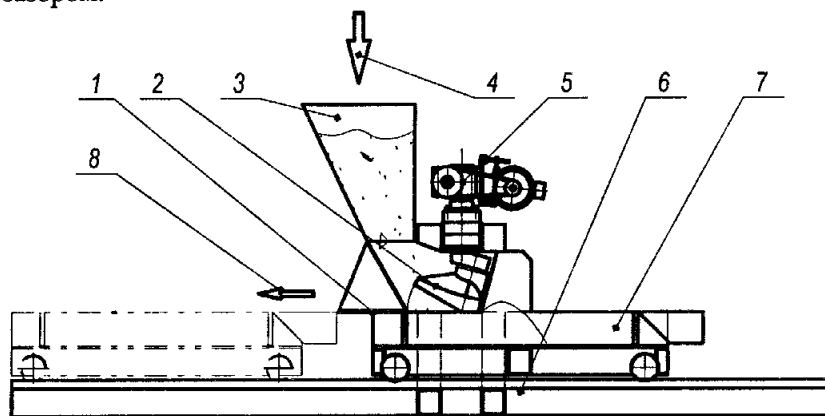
Конструктивная схема нагнетателя с конусной рабочей поверхностью:
